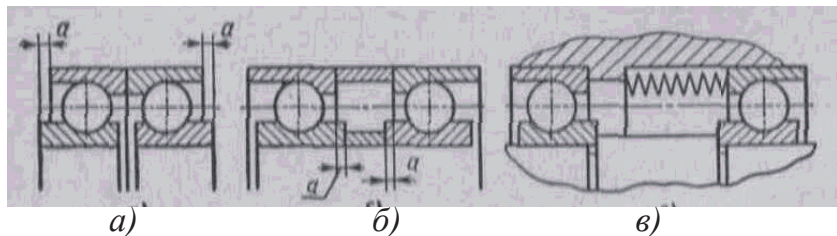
Способы создания натяга в подшипниковых опорах.
